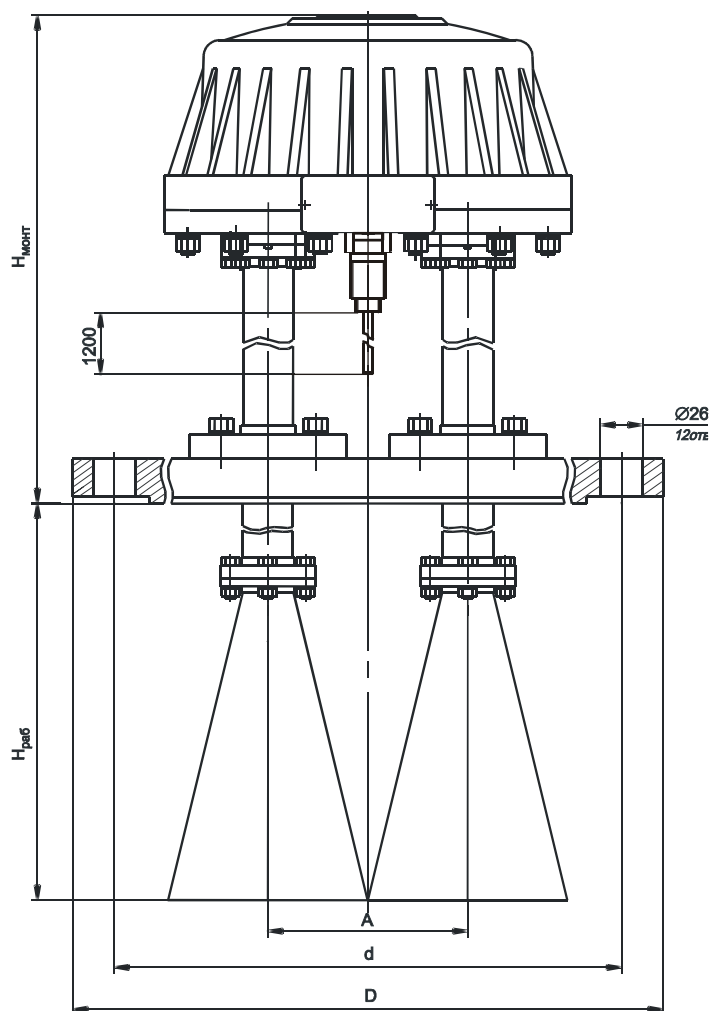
Габаритные и установочные размеры приборов БАРС 352 И. 12 и БАРС 352 И.14
